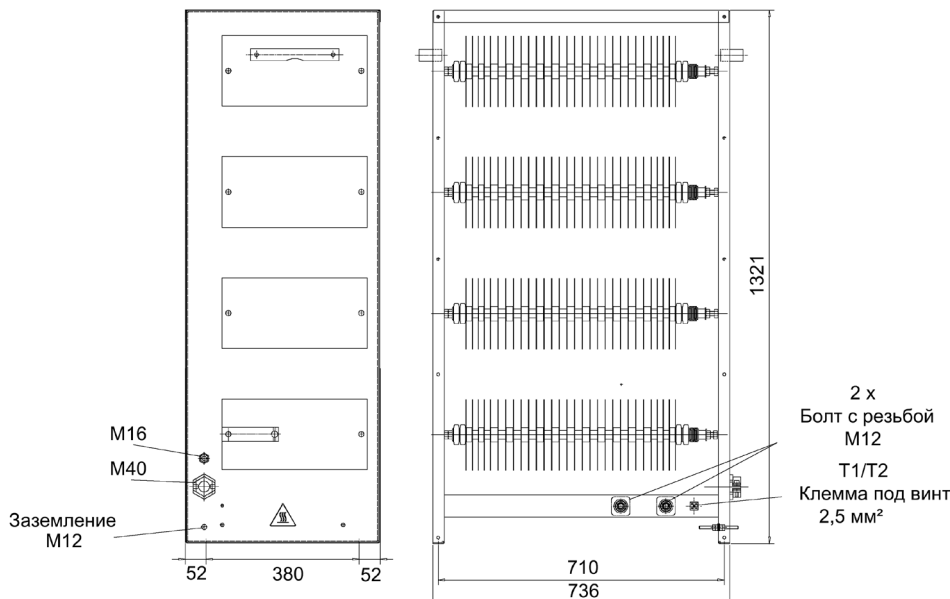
Габаритный чертеж тормозного резистора 50 кВт
